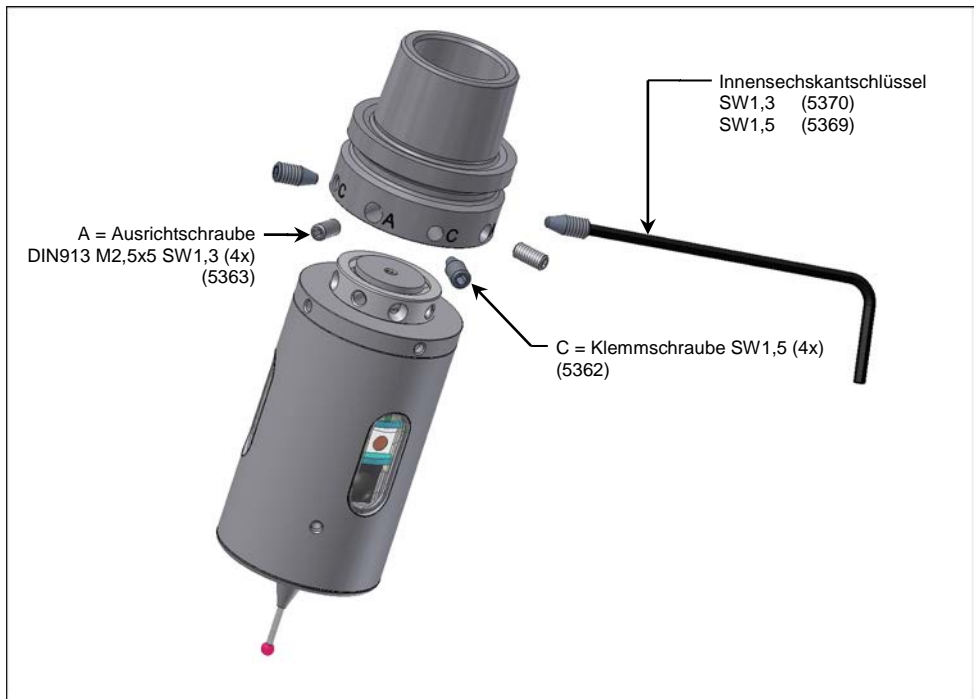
Montage/Demontage der Werkzeugaufnahme
